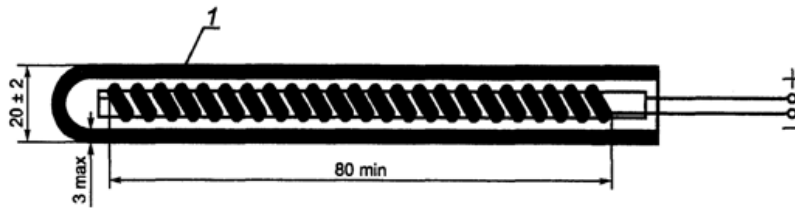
Випробувальний розжарювальний стрижень
